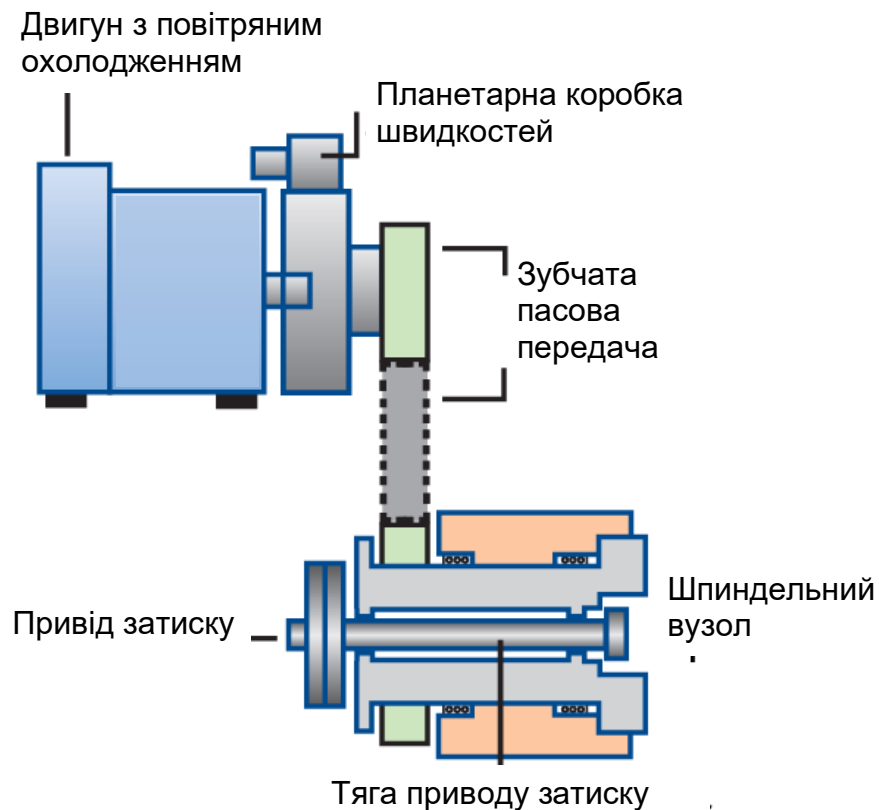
Модернізований привод головного руху токарно-револьверного багатоопераційного автомата з ЧПК мод. 11Б40ПФ4
